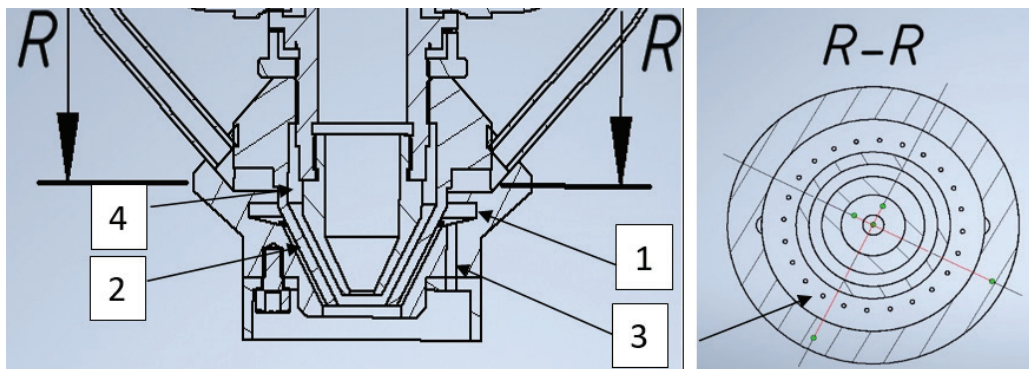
Конструктивне утворення каналів в розробленій лазерній головці: 1 – камера захисного газу; 2 – канал між соплами; 3 – отвори між камерою та захисним ковпаком; 4 – канал подачі порошку
